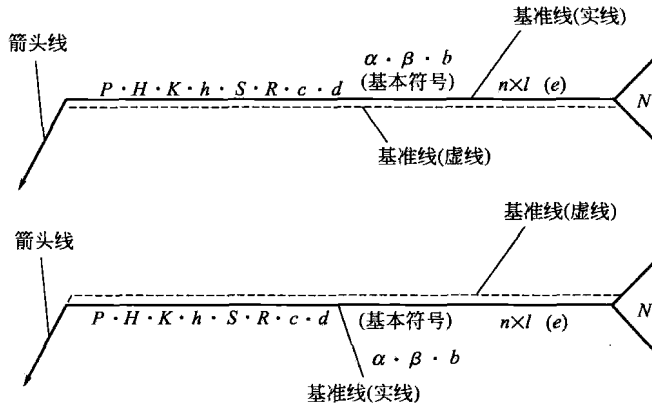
焊缝尺寸符号及数据的标注原则
